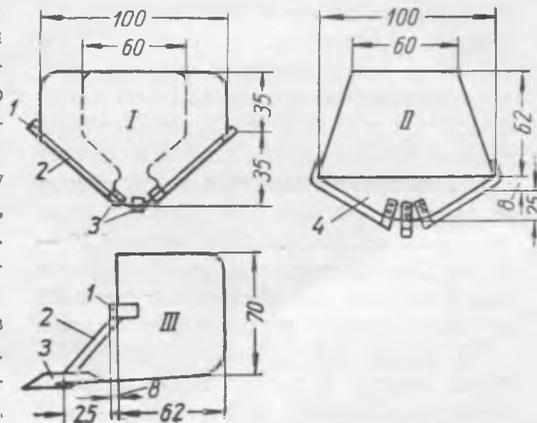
Схема устройства ковша для экскаватора: I — профиль по линии режущих граней; II — план; III — продольный профиль; 1 — отбойный полозок; 2 — нож-откосник; 3 — зубья заглубителя; 4 — режу-
